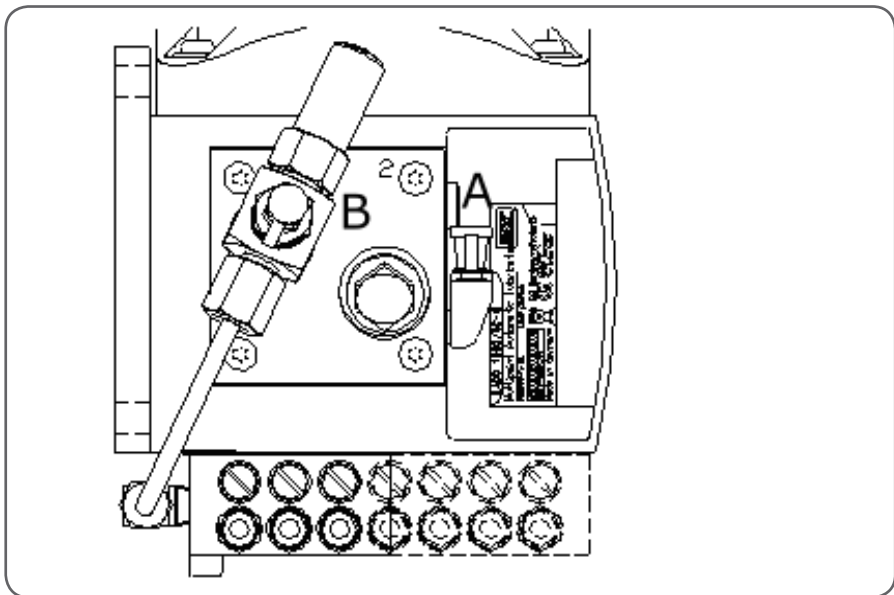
Posição dos bocais de massa lubrificante para enchimento e purga.
